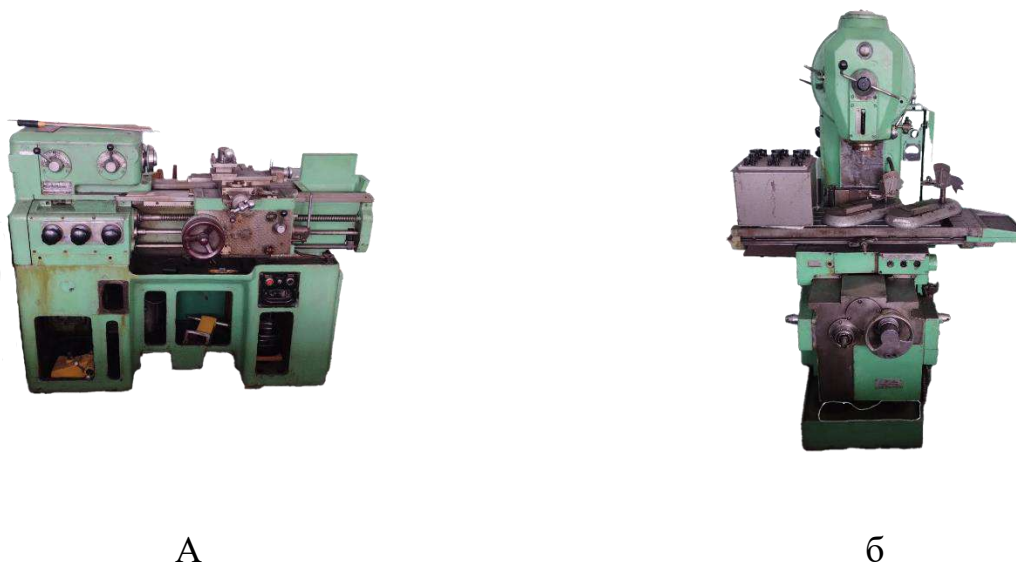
Обладнання для механічної обробки виробів із полімерів: а – токарний верстат; б – свердлильно-фрезерний верстат
